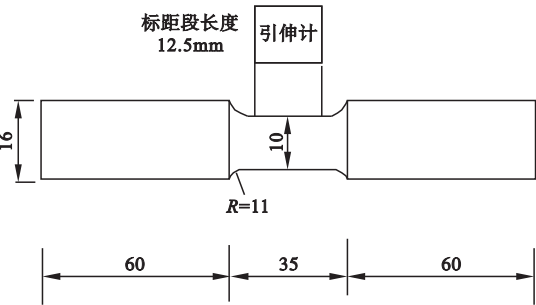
母材、焊缝标准圆棒试件几何尺寸
